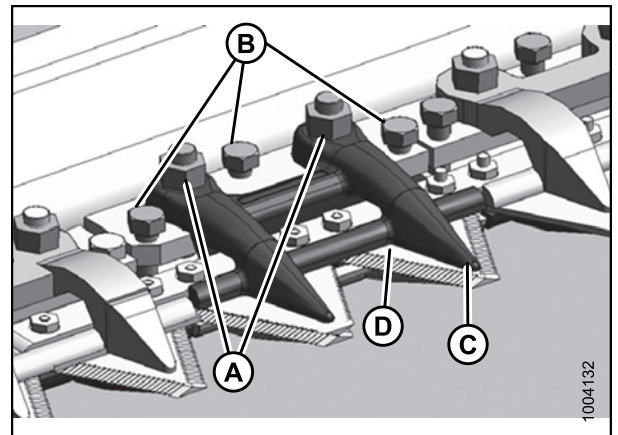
Тупой противорежущий палец — двойной нож
